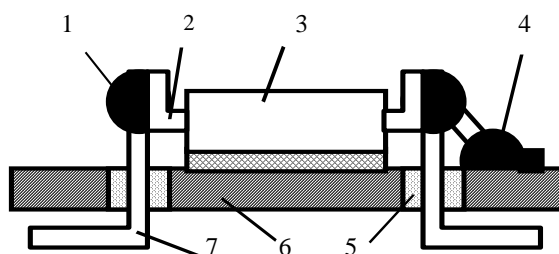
Фрагмент конструкции теплопроводящей платы проводного монтажа:
